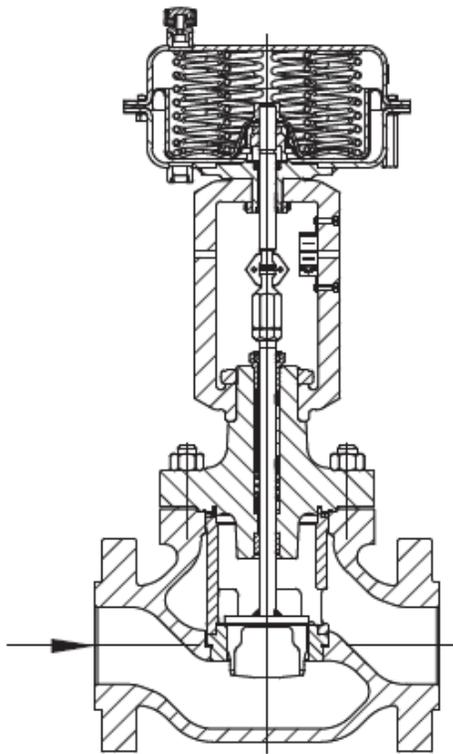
· Регулирующий клапан с фланцами тип 3291-1 с пневматическим приводом тип 3271
